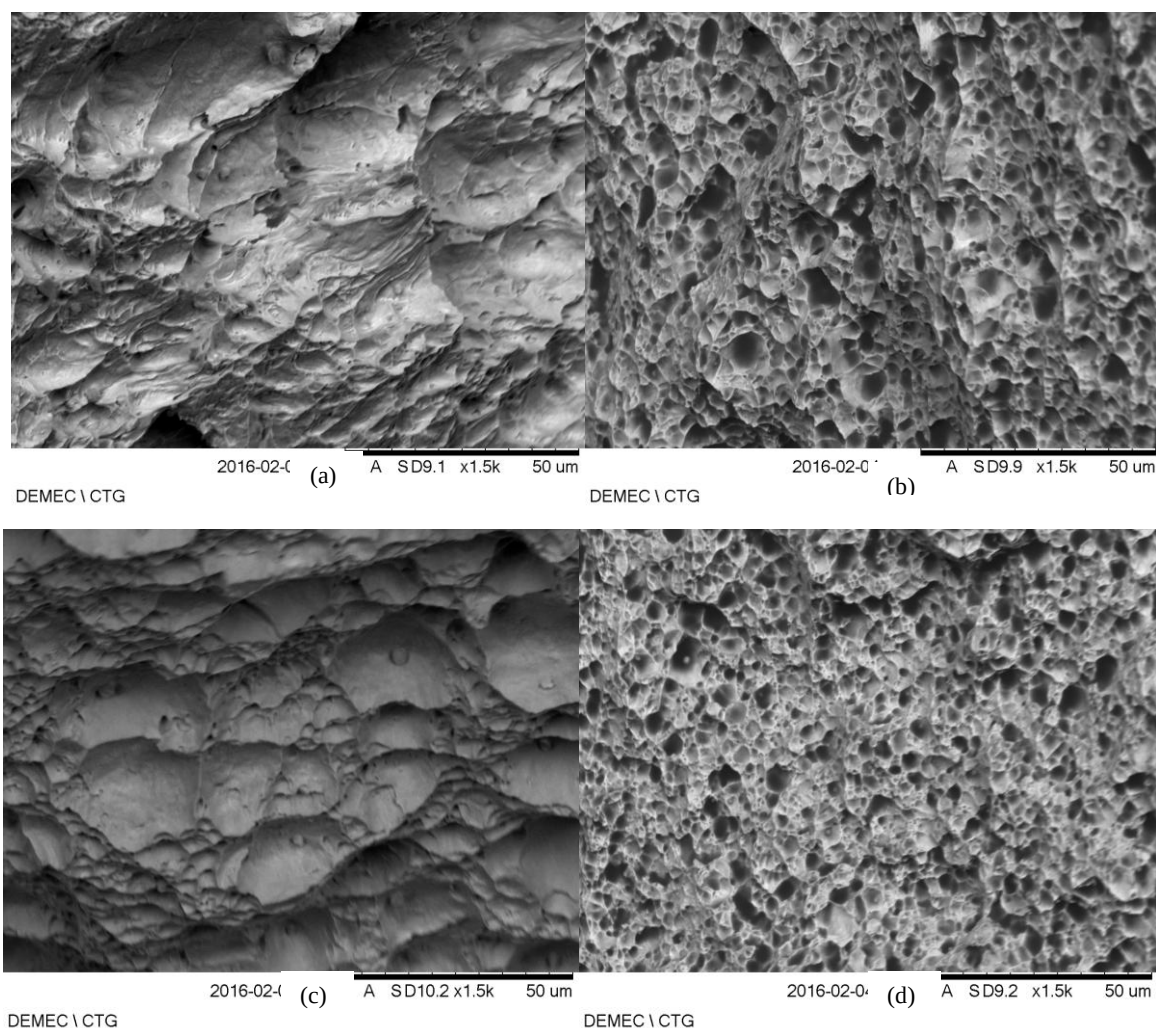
MEV das superfícies das fraturas do ensaio de impacto dos corpos de prova como recebido, sem solda (a); como recebido, com solda (b) após processo de corrosão, sem solda (c); após processo de corrosão, com solda (d).
